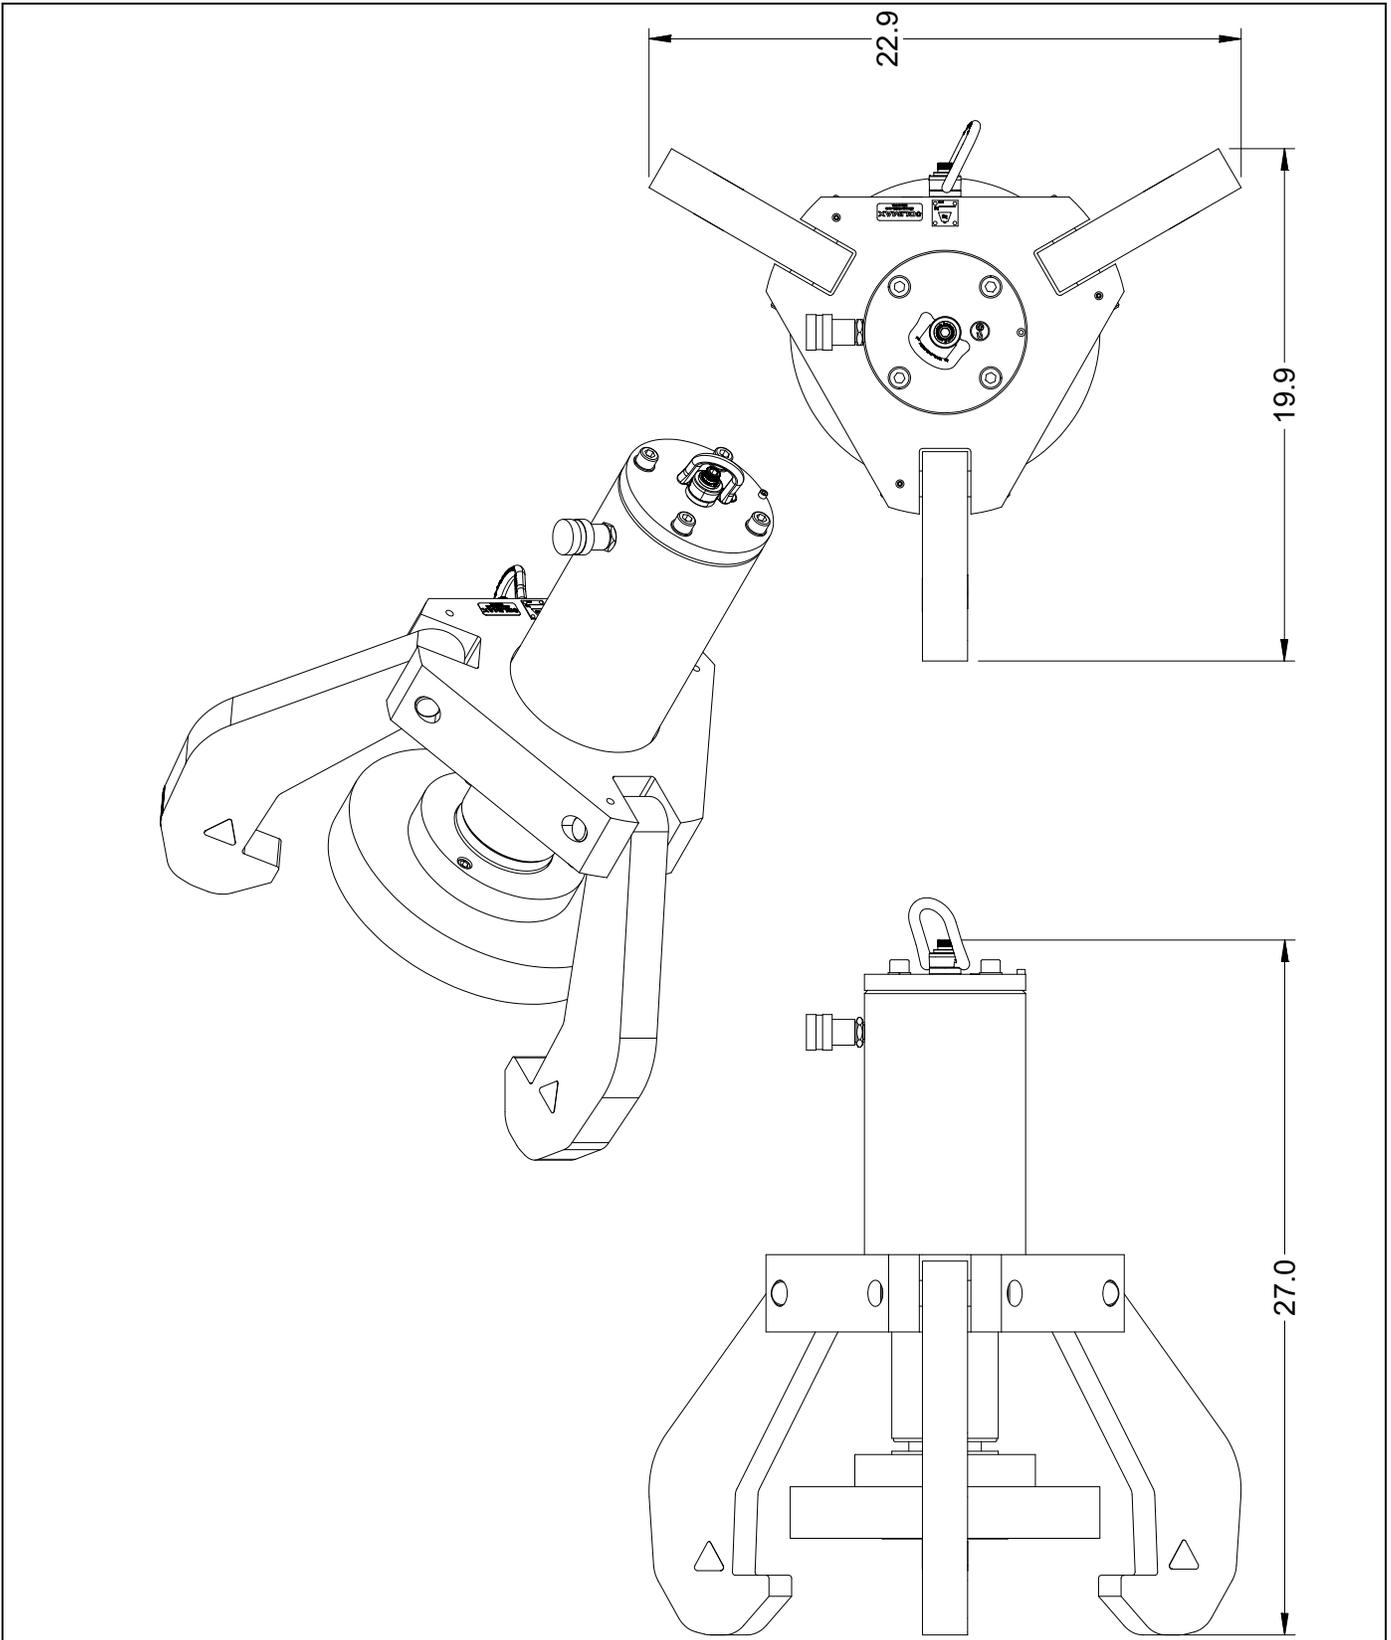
DIMENSIONS DE LA HFS-10
